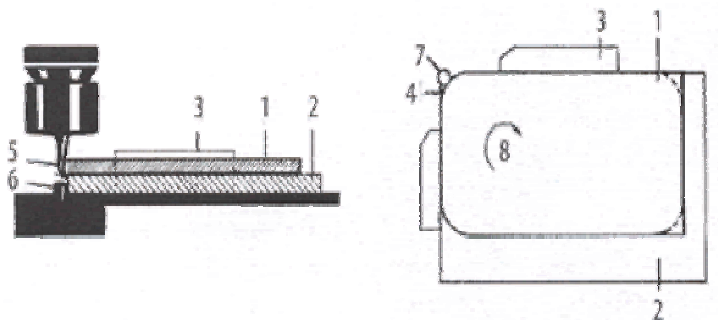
Принцип верхнего фрезерования по шаблону: 1=заготовка, 2=направляющая опора, 3=ограничитель, 4=шаблон, 5=направляющий стержень, 6=фреза, 7=рабочая зона фрезы, 8=подача
